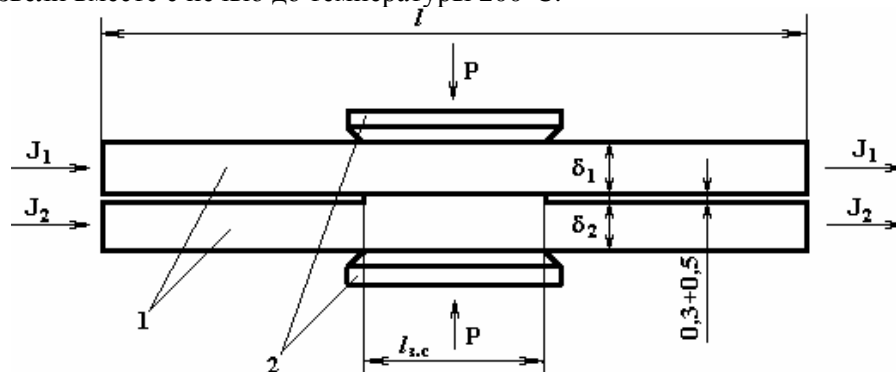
Схема обработки импульсным током свариваемых образцов. 1 – образцы; 2 – зажим приспособления; $l_{з.с}$ – длина зоны сварки; l – длина образца; δ_1, δ_2 – толщина образца
